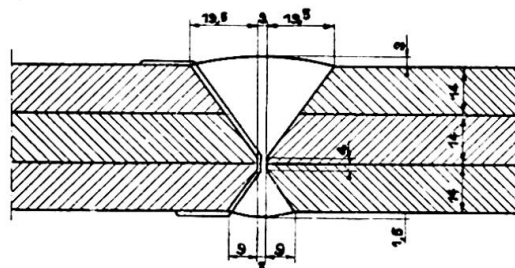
Coupe des cordons de soudure de la partie au droit des cornières.
